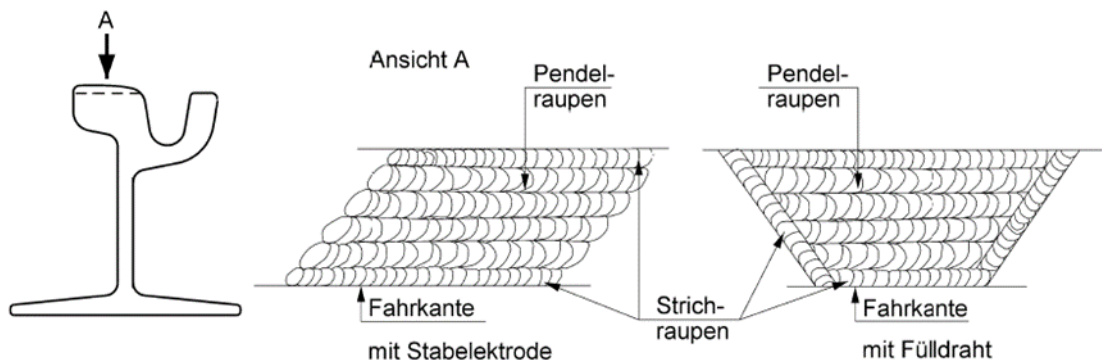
Ausführung der Reparaturschweißung
